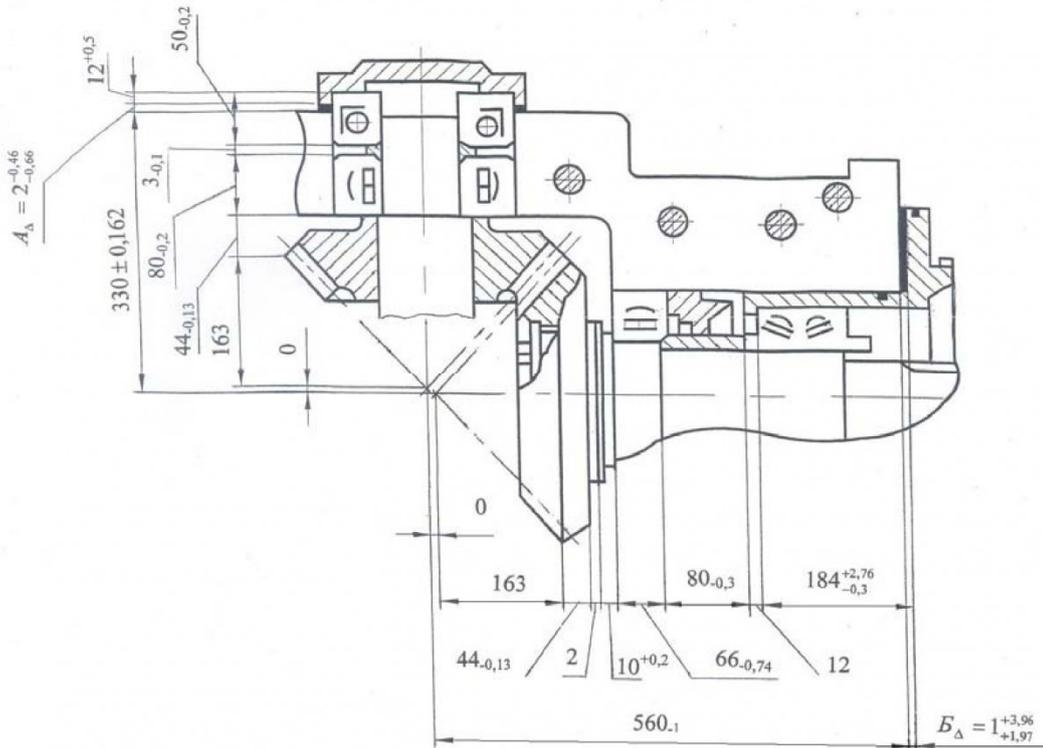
Схемы размерных цепей, определяющих точность совпадения вершин делительных конусов конических зубчатых колес редуктора скребкового конвейера
